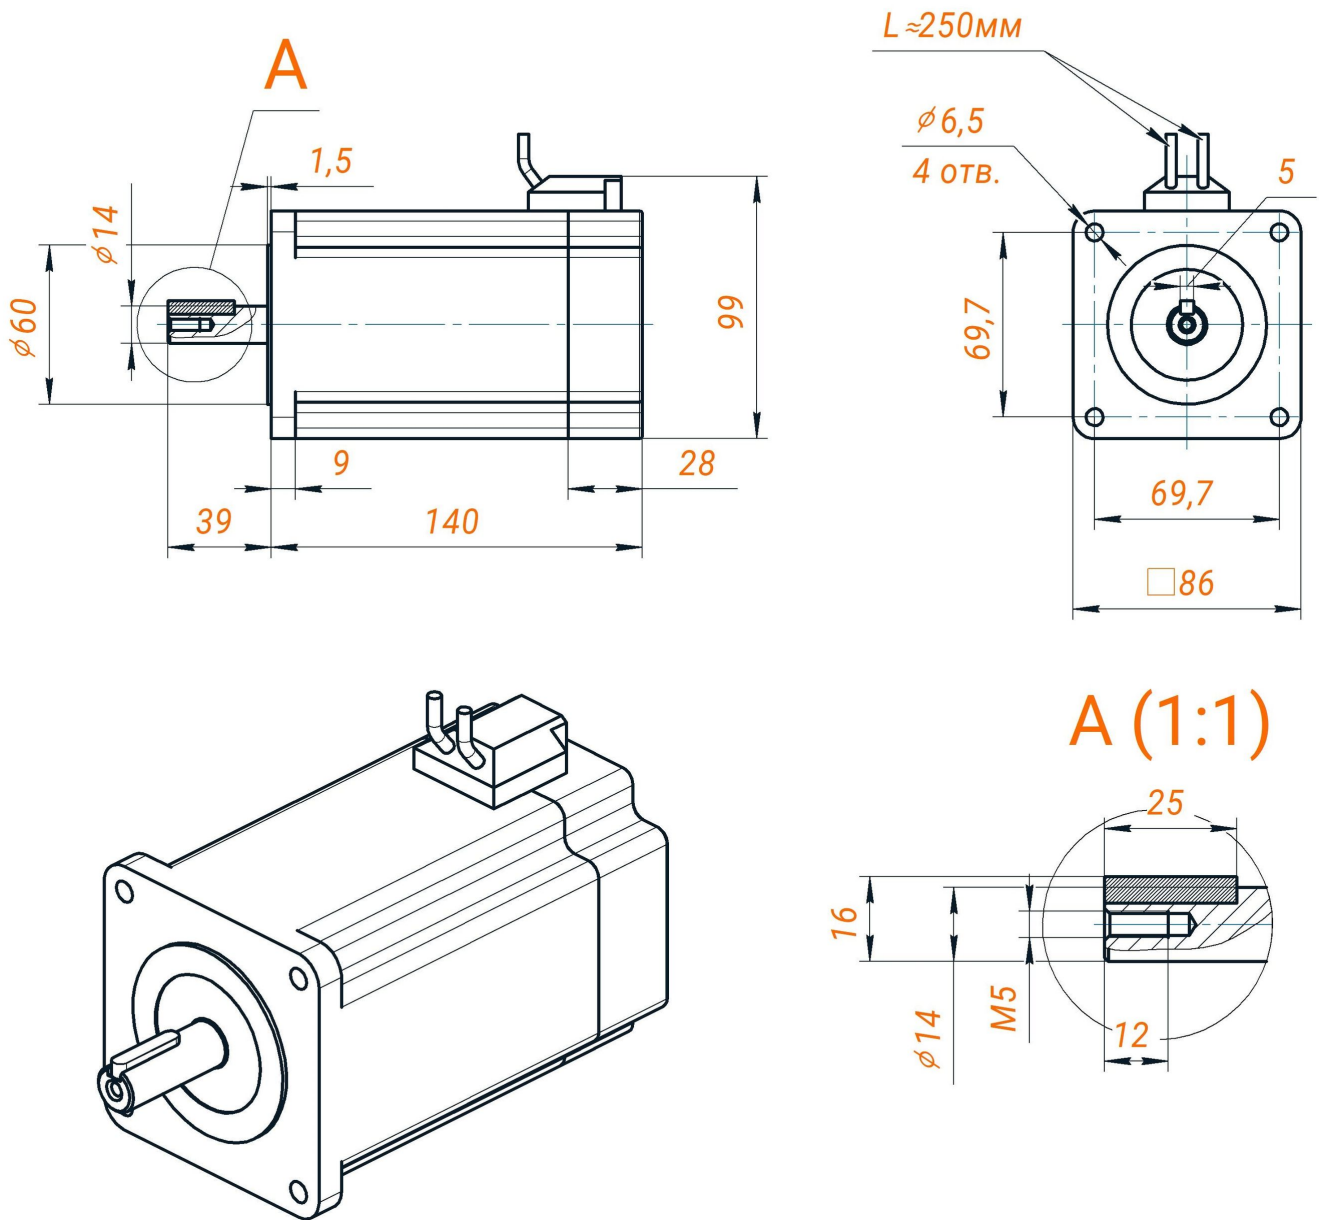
Габаритные размеры шагового серводвигателя YK286EC118A1
